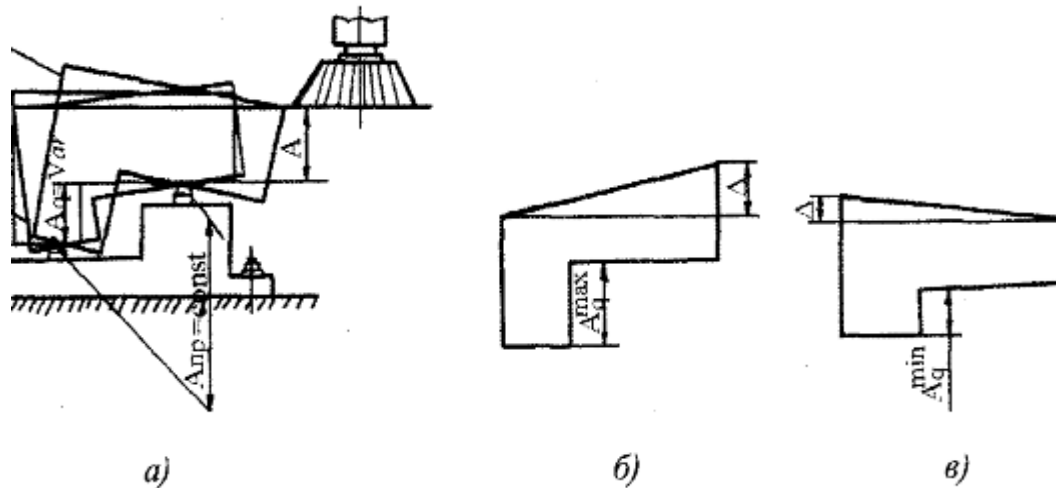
Невизначеність базування заготовки при обробці та її вплив на точність обробки
